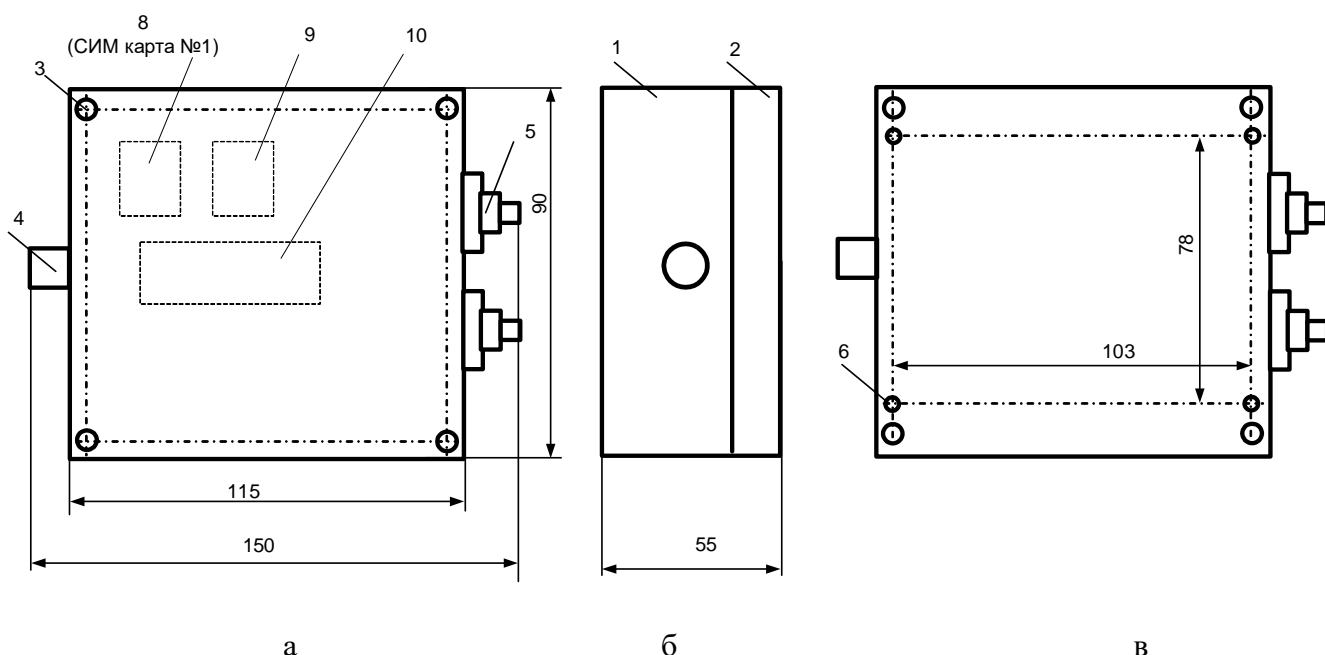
Габаритные (а и б) и установочные (в) размеры GSM регистратора
